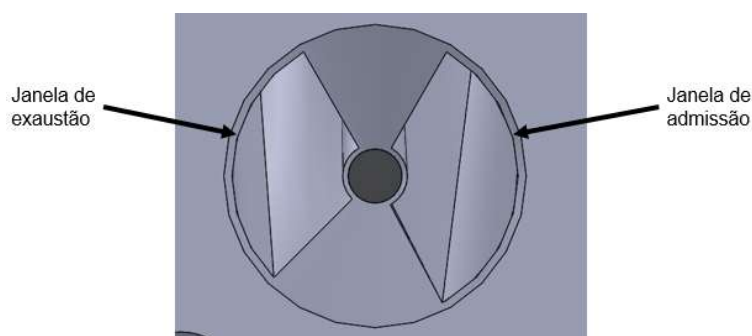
Vista em perspectiva do conjunto do cabeçote
